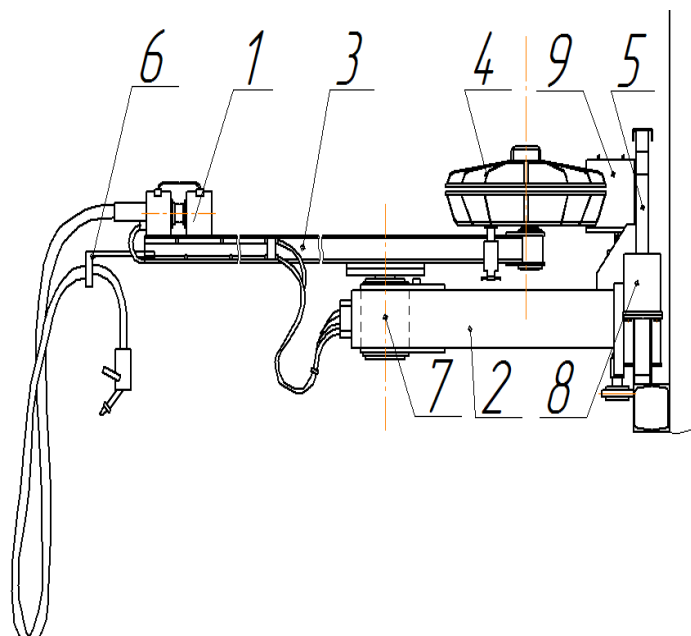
Приспособление для сварки балки концевой:
